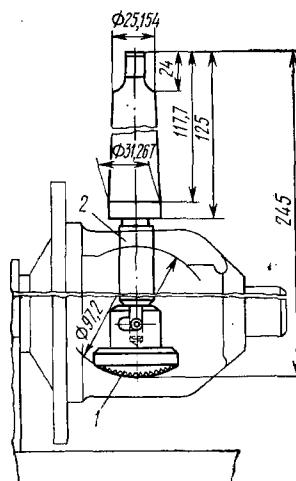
Сборная оправка для зачистки задиров и износов на сфере коробки дифференциала:
